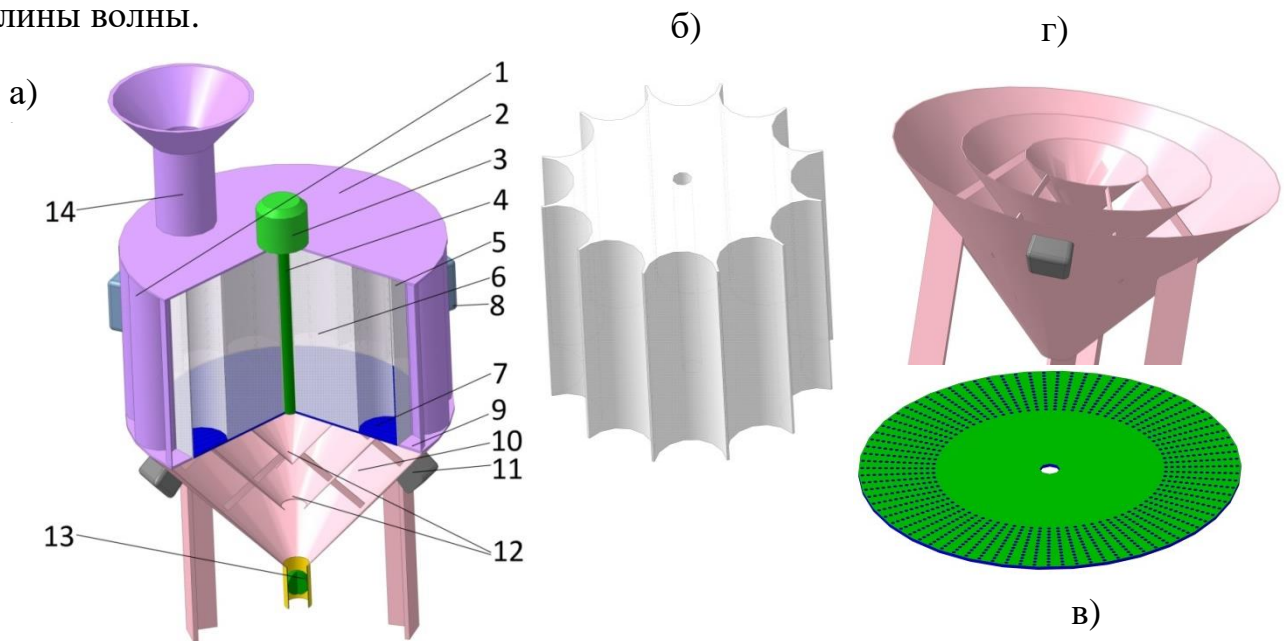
СВЧ-размораживатель непрерывно-поточного действия с металлодиэлектрическим резонатором для дефростации и разогрева молозива животных: а) общий вид; б) диэлектрический сплошной цилиндр; в) диск неферромагнитный перфорированный; г) конический неферромагнитный резонатор с радиопрозрачными усеченными коническими тарелками; 1 – экранирующий неферромагнитный цилиндрический корпус; 2 – верхнее неферромагнитное основание; 3 – электродвигатель; 4 – вал неферромагнитный; 5 – радиопрозрачный пустой цилиндр; 6 – диэлектрический сплошной цилиндр; 7 – диск неферромагнитный перфорированный; 8, 11 – магнетроны; 9 – кольцевое неферромагнитное основание корпуса; 10 – конический неферромагнитный резонатор; 12 – радиопрозрачные усеченные конические тарелки; 13 – запердельный волновод с шаровым краном; 14 – запердельный волновод для приема сырья
